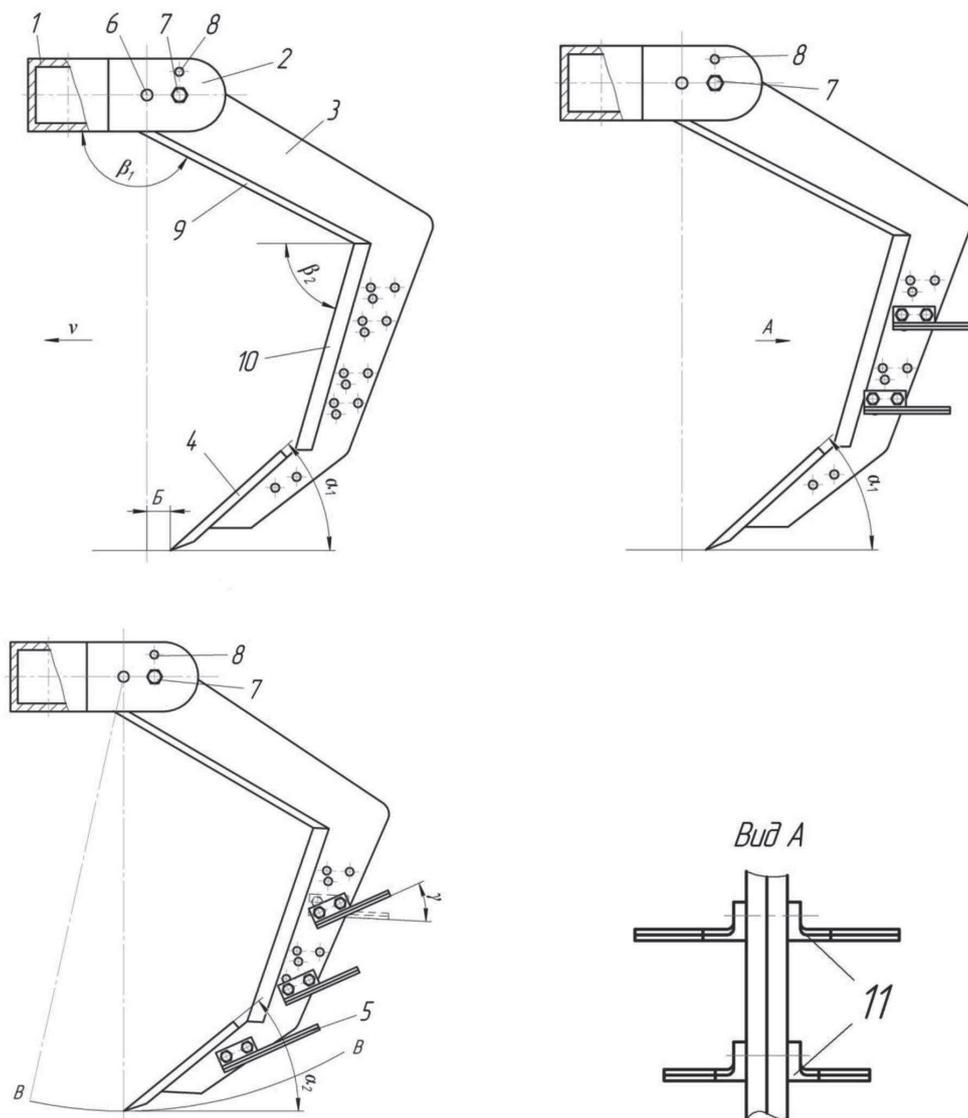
Схема глубокорыхлителя: а – при рыхлении подпахотного слоя почвы, вид сбоку; б – при выполнении рыхления пахотного слоя, вид сбоку; в – при выполнении рыхления подпахотного и пахотного слоя, вид сбоку; г – вид А; 1 – рама; 2 – кронштейн; 3 – стойка; 4 – наральяник; 5 – боковой нож; 6 – ось; 7 – срезной болт; 8 – отверстие; 9, 10 – режущая кромка; 11 – Г-образный боковой нож
